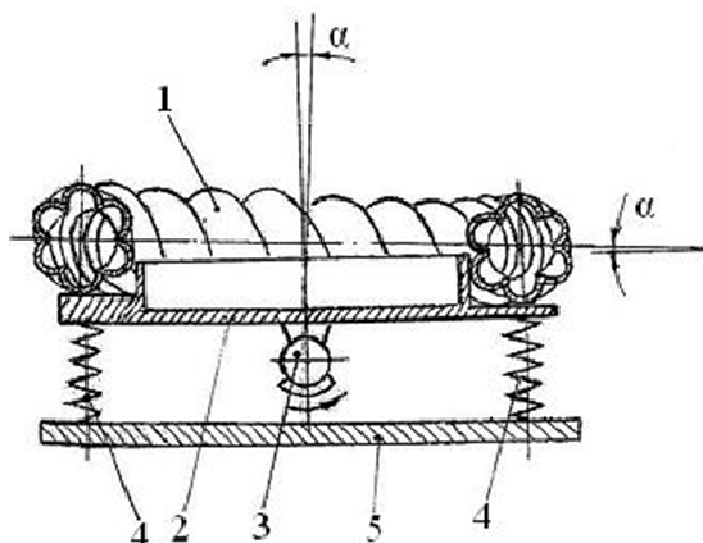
Установка вибрационная для приготовления кормов
